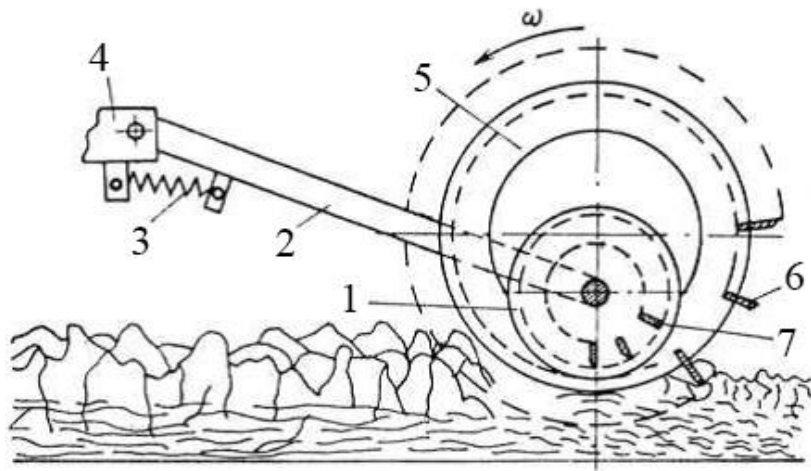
Конструктивна схема ґрунтообробного знаряддя: 1, 5 – внутрішній і зовнішній барабани; 2 – шарнірний поводок; 3 – пружинний довантажувач; 4 – рама культиватора; 6, 7 – радіальні планки барабанів [5].
